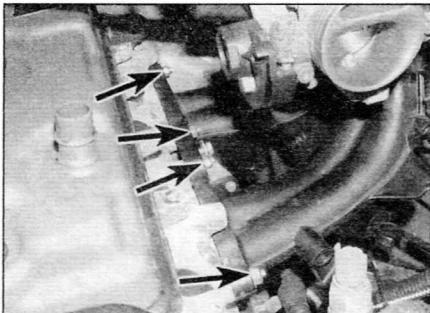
Верхние гайки крепления впускного коллектора (отмечены стрелками) (показана модель с двигателем 1.4 л)
